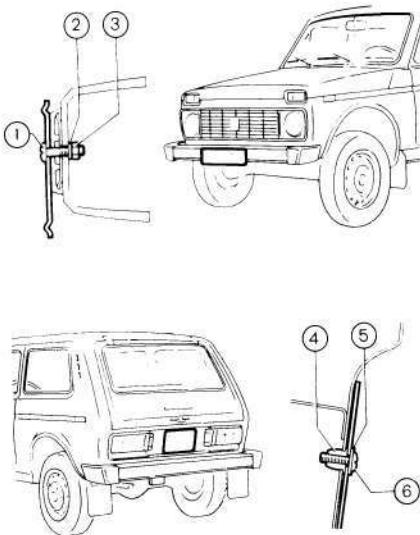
Крепление номерных знаков: 1,6 — винты;
